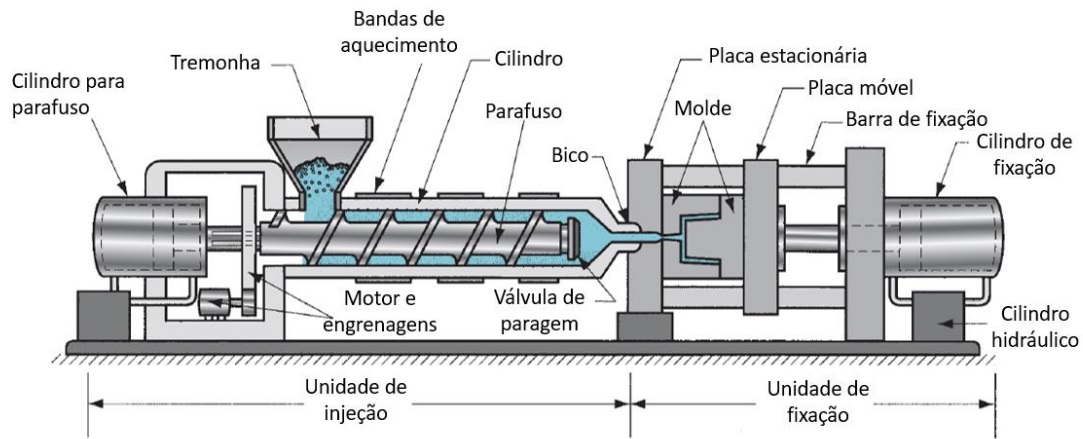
Esquema representativo de uma máquina de moldação por injeção (adaptado de [8]).
